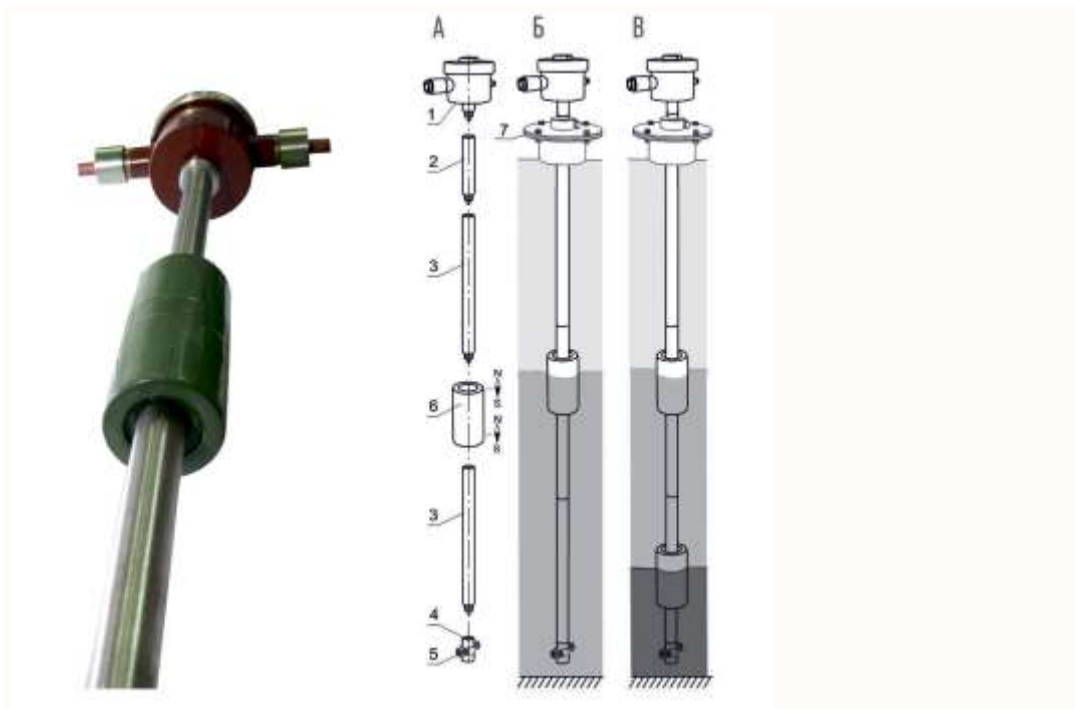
Преобразователь магнитный поплавковый ПМП-128, его конструкция
